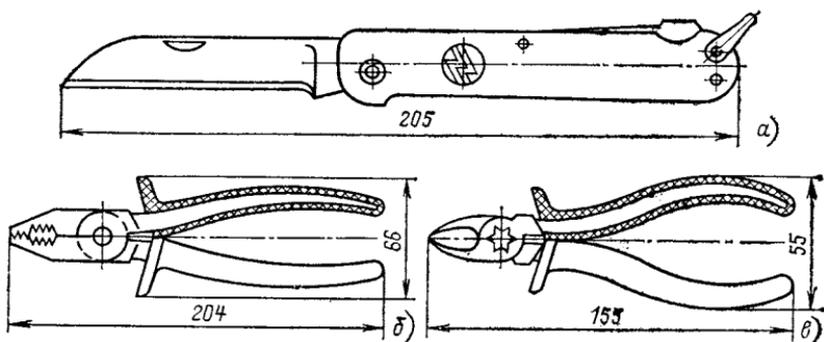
Ручные электромонтажные инструменты общего назначения; а — нож монтерский; б — плоскогубцы комбинированные; в — бокорезы
